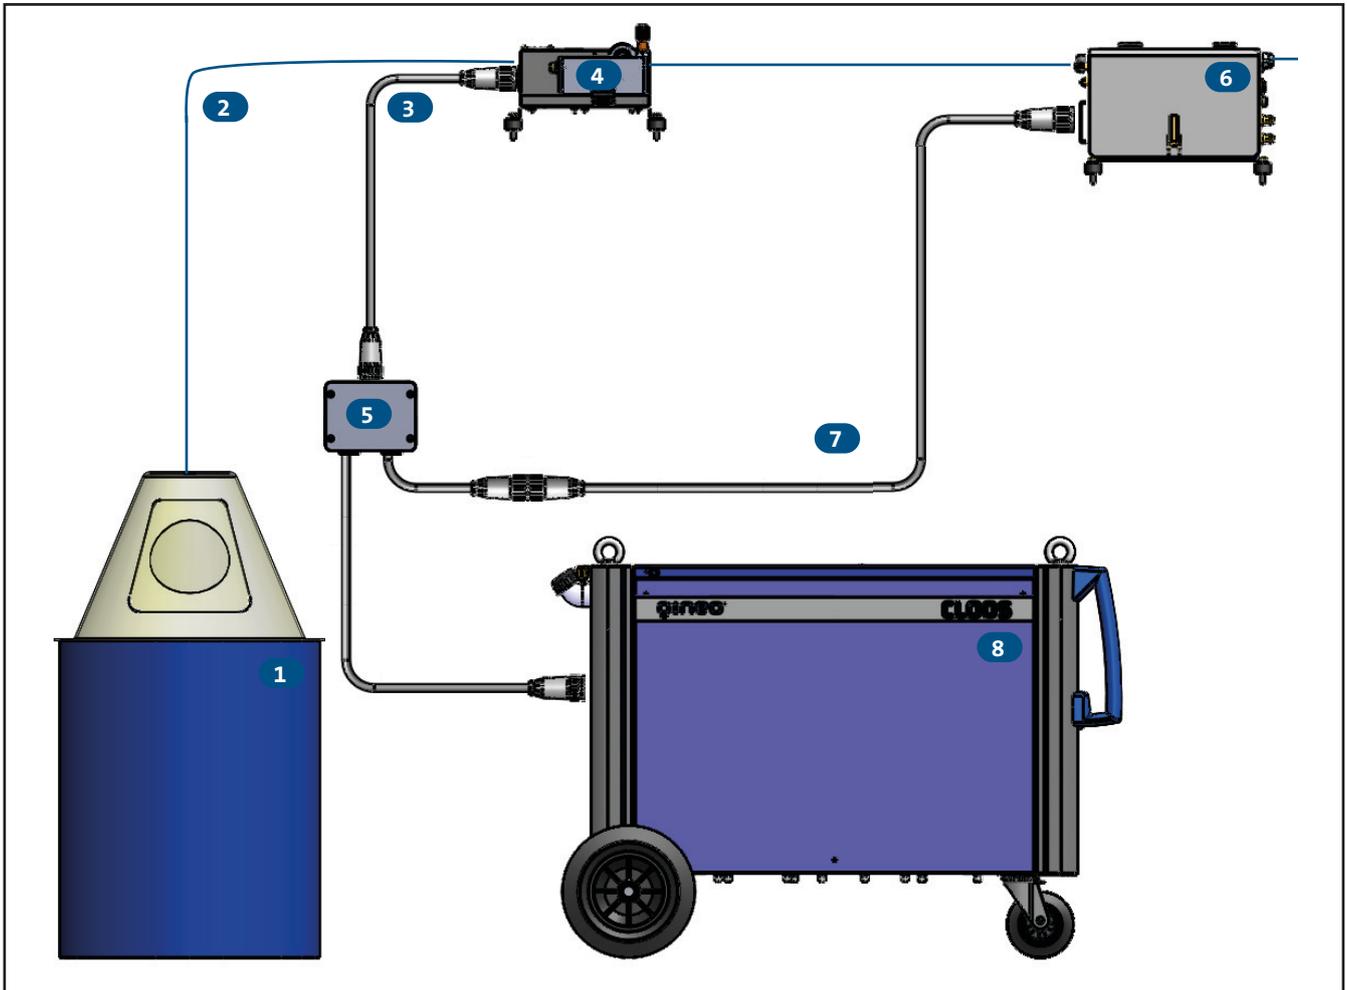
QWD-B Anschlusschema für den Eindrahtschweißprozess
